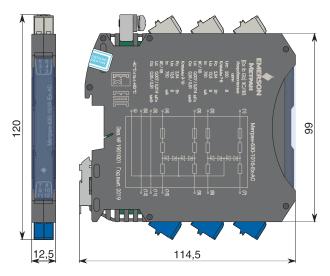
Габаритные размеры барьера с разъемами с пружинными клеммниками и тестовыми гнездами
